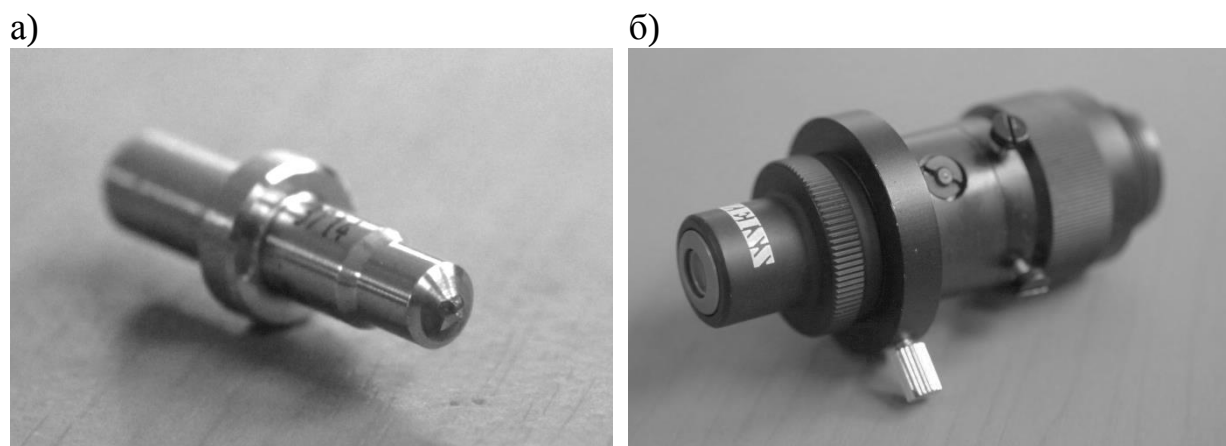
Приспособления для измерения твердости по методу Виккерса для твердомера DIGI-TESTOR 971/3000D:
